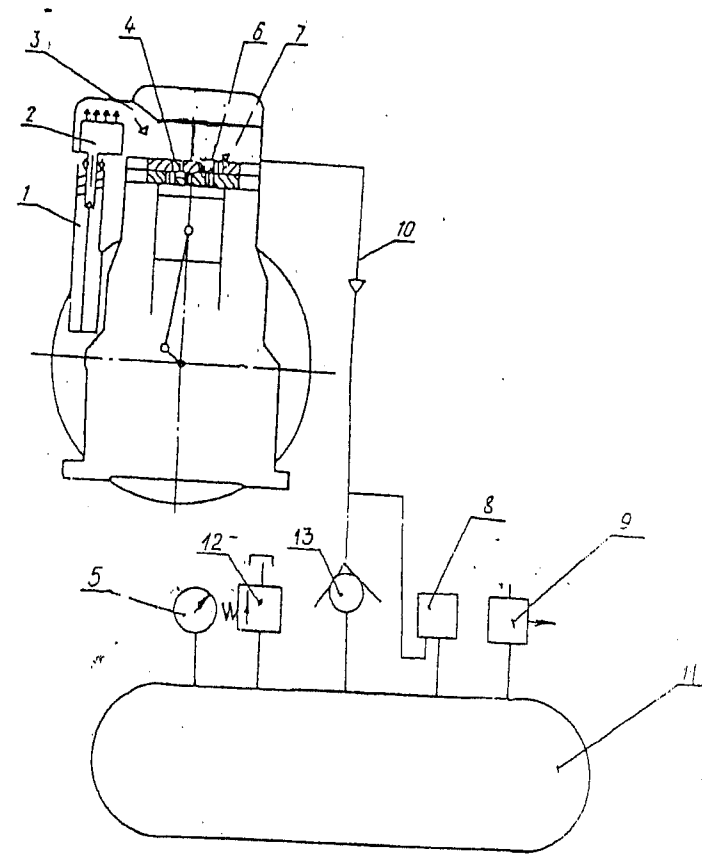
Компрессор установки СО62А-2А и СО-62А-12А
